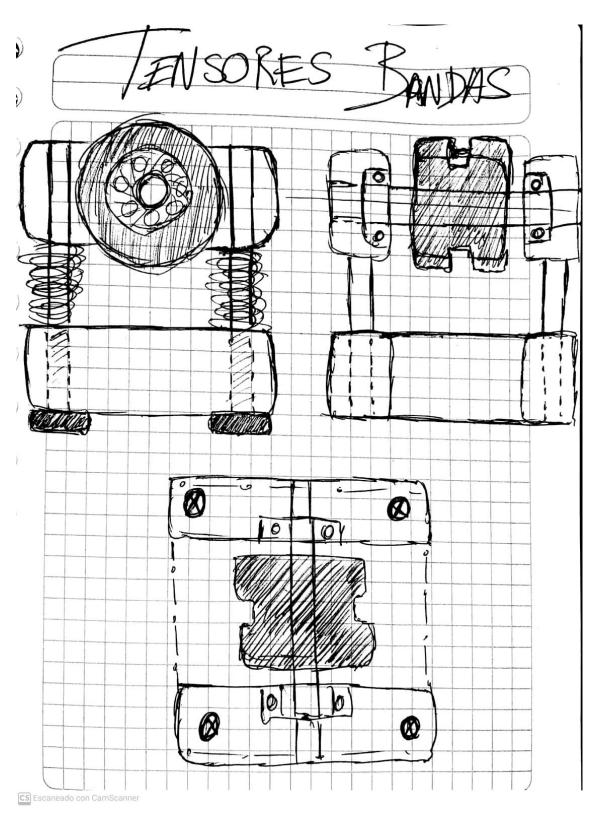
Sketch de detalle de la propuesta para el sistema de tensión.
